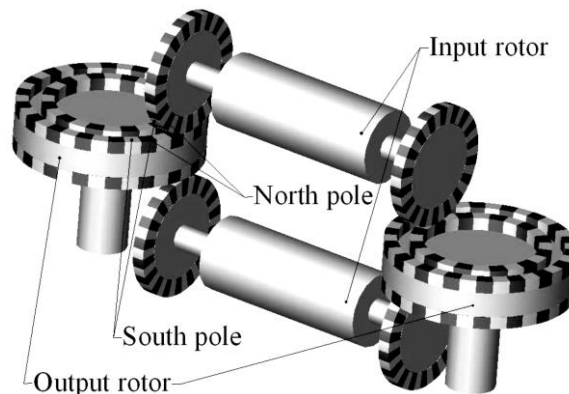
Engrenage magnétique à deux arbres [HEN02].
